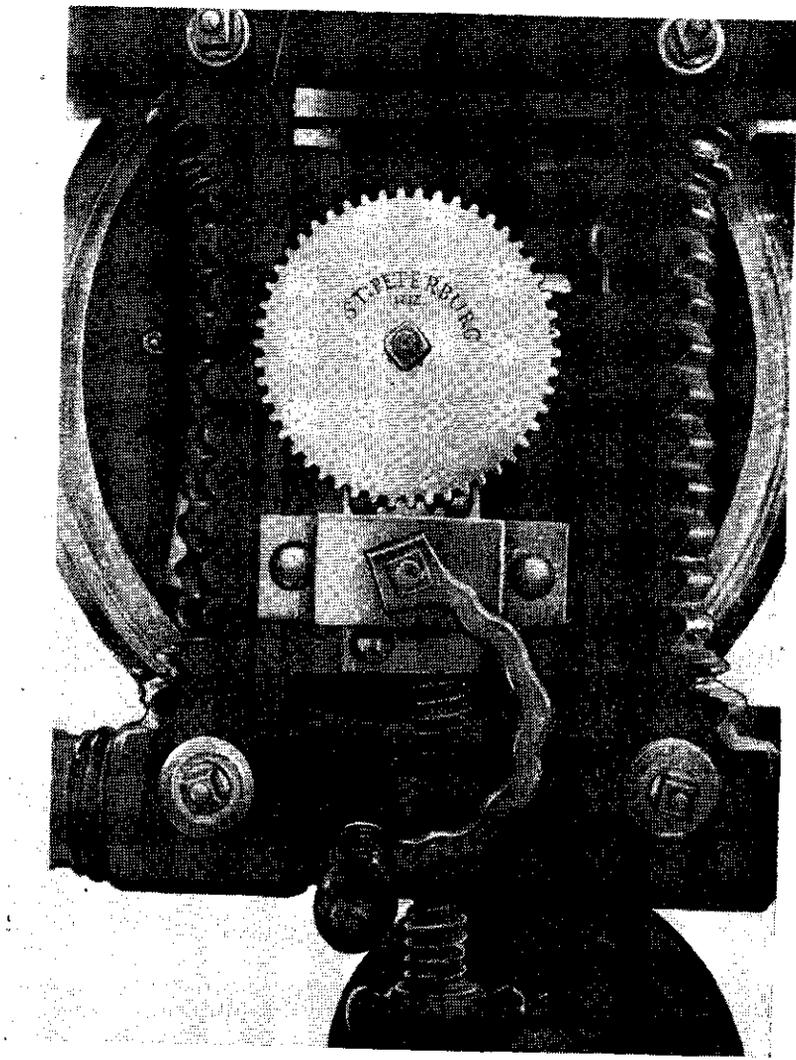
Узел приводной рукоятки с зубчатой передачей на верхний приводный вал токарно-копировального станка 1712 г.
